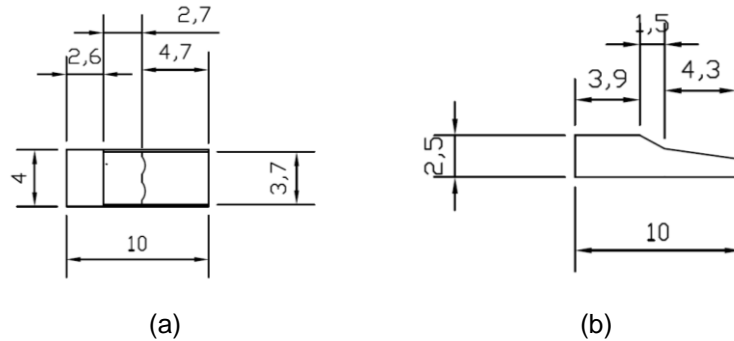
Dozer placa ancha (a) Vista en planta (b) Vista longitudinal.
